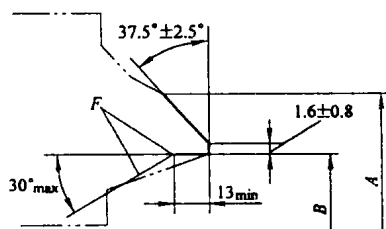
有断裂长方形衬环接头的焊接端
